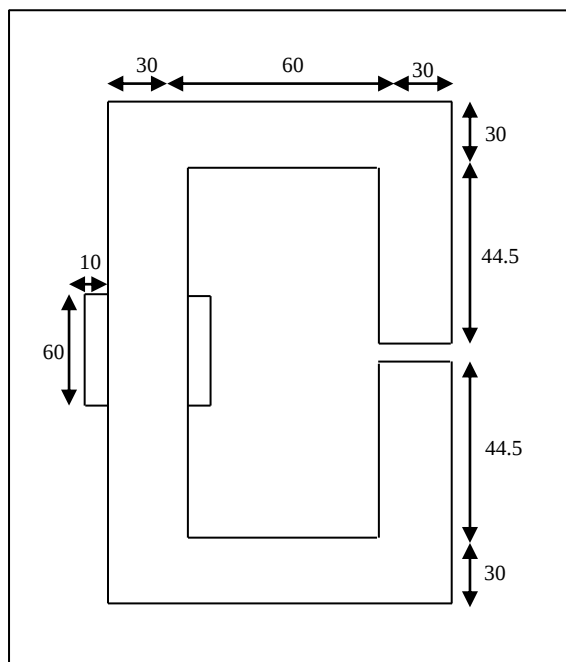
Dimensions géométriques de la bobine à noyau de fer
